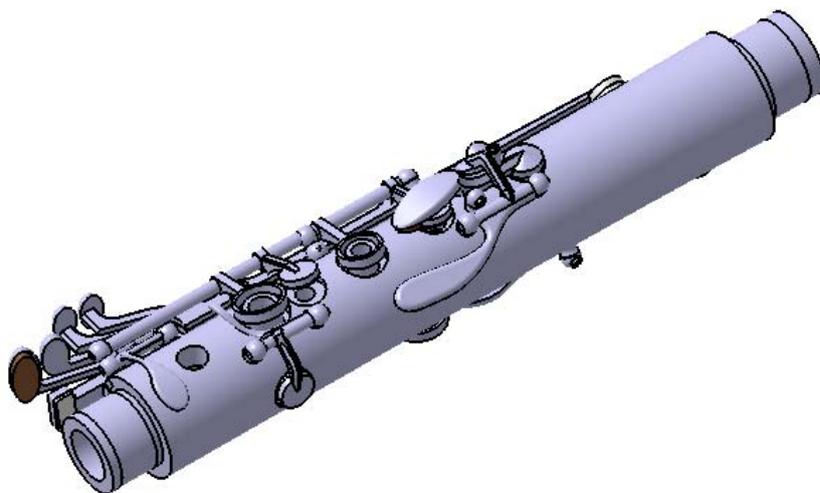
Ensamblaje del cuerpo superior. Segunda vista.
